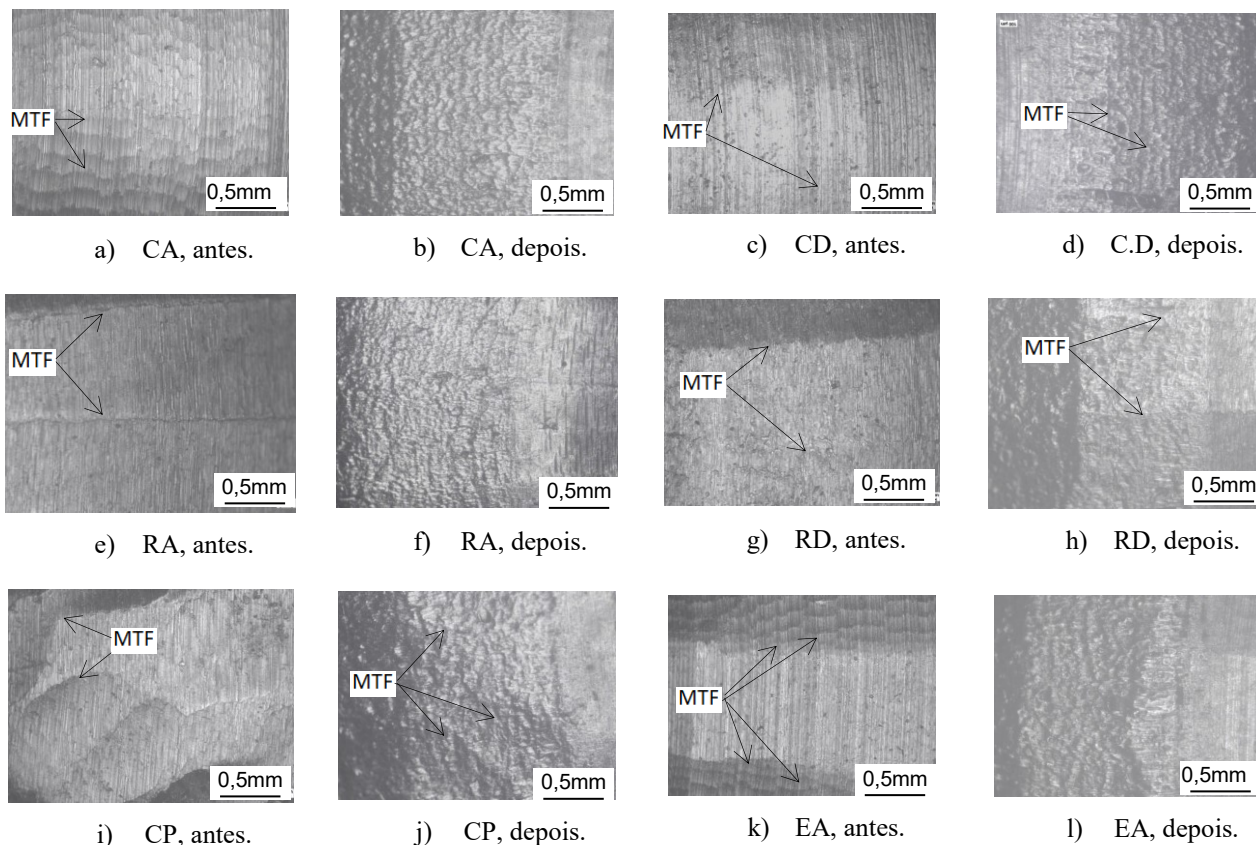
Imagens das superfícies usinadas antes e após o processo de estampagem a quente.
